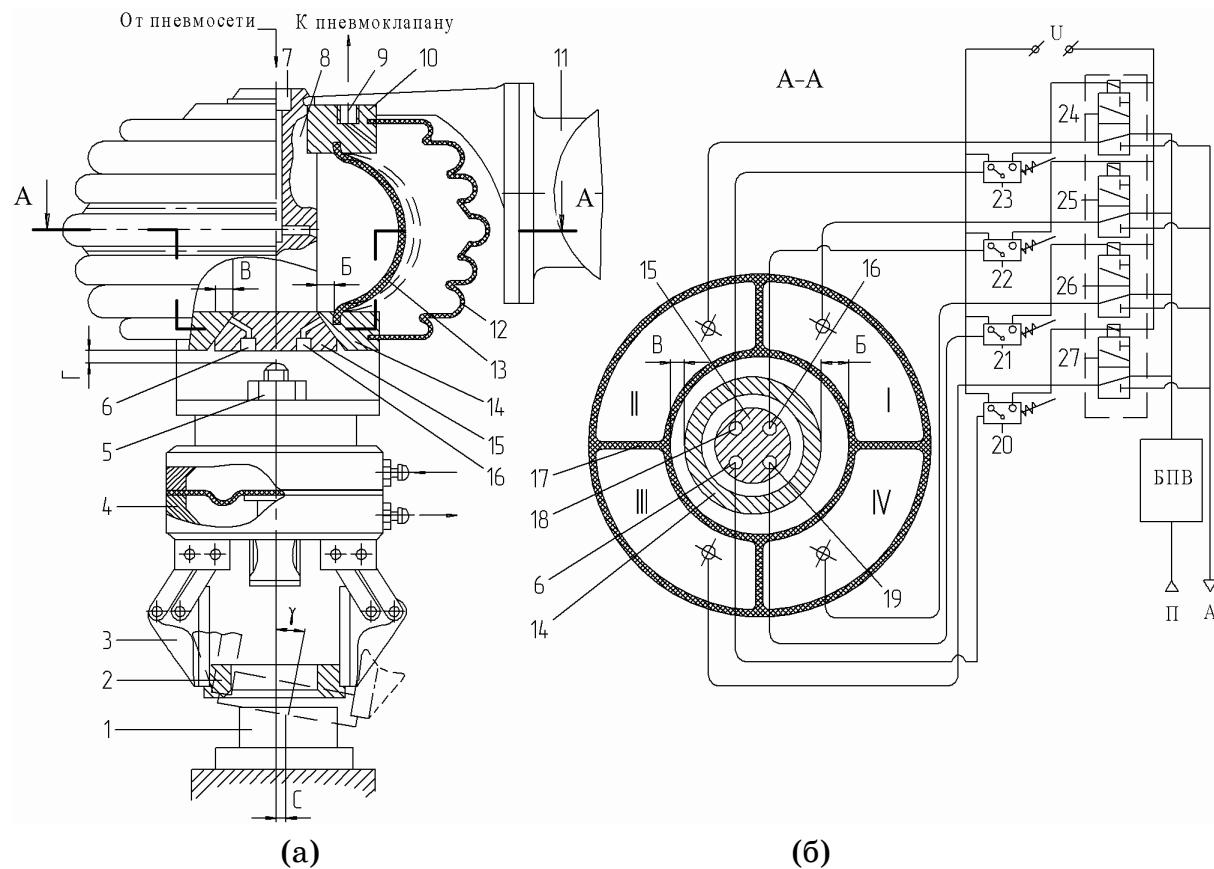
Конструкция (а) и схема блока управлени (б) адаптивного сборочного модуля манипулятора
